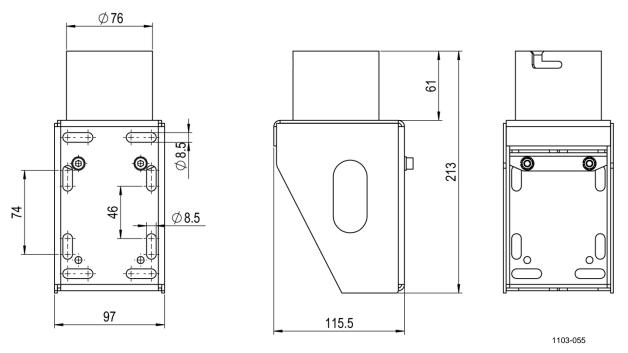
Размеры комплекта установки FIX70 в миллиметрах
